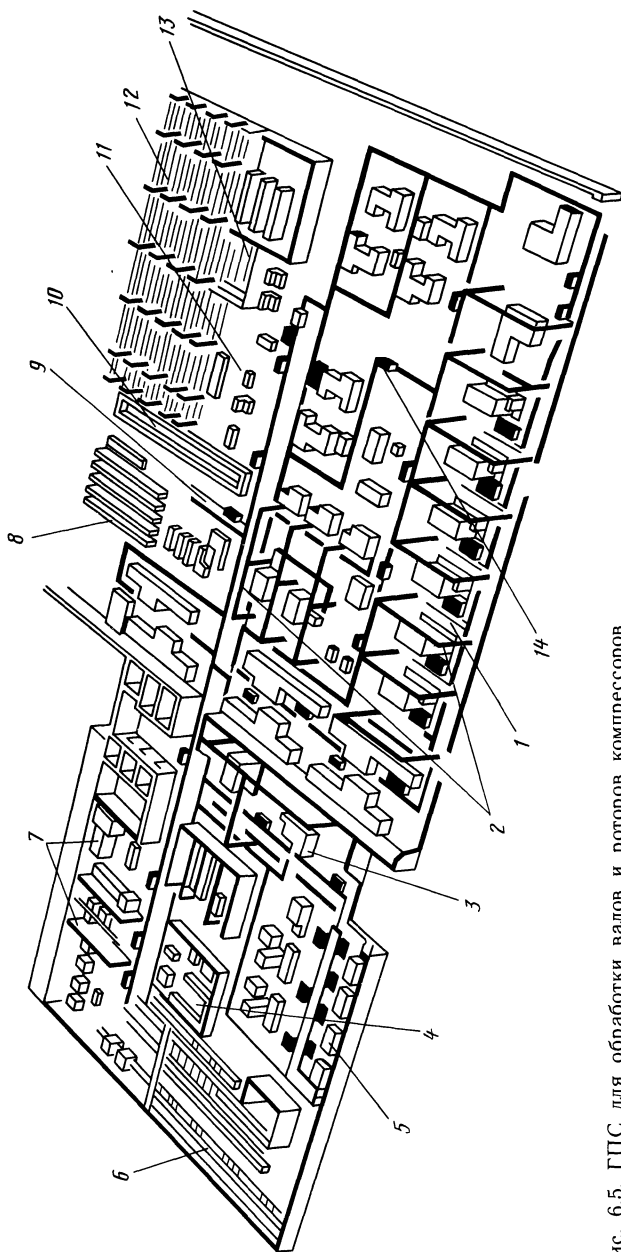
ГПС для обработки валов и роторов компрессоров турбин:
